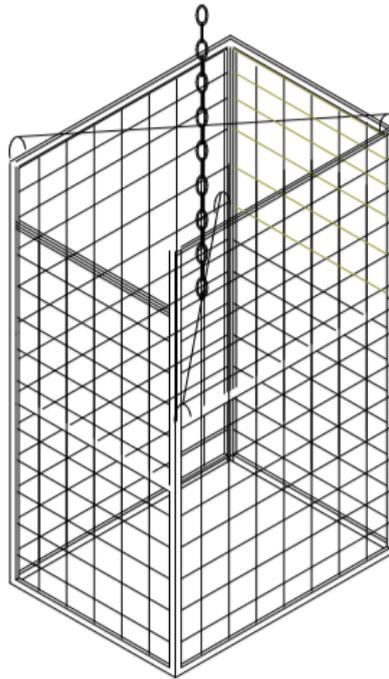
Canastilla actualizada con dimensión de 0.65x0.40x0.40m
